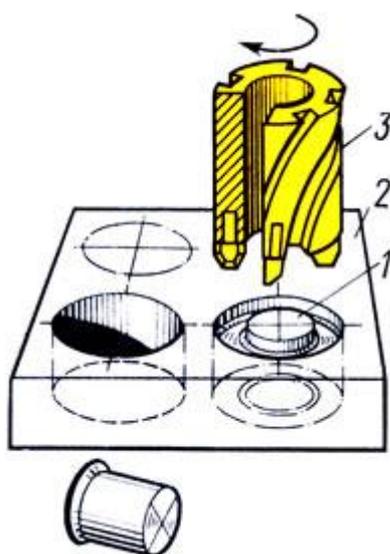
Кольцевое сверление: 1 - сердцевина детали (стержень), 2 - деталь, 3 - кольцевое сверло (резец)
